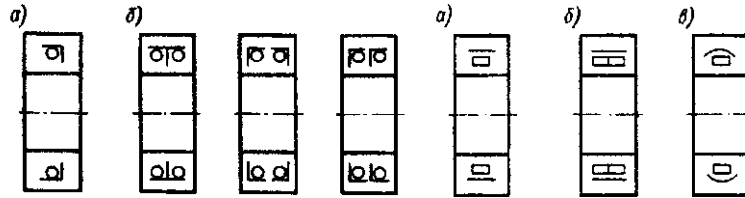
Шариковый подшипник радиально-упорный: *a* — однорядный; *b* — двурядный
